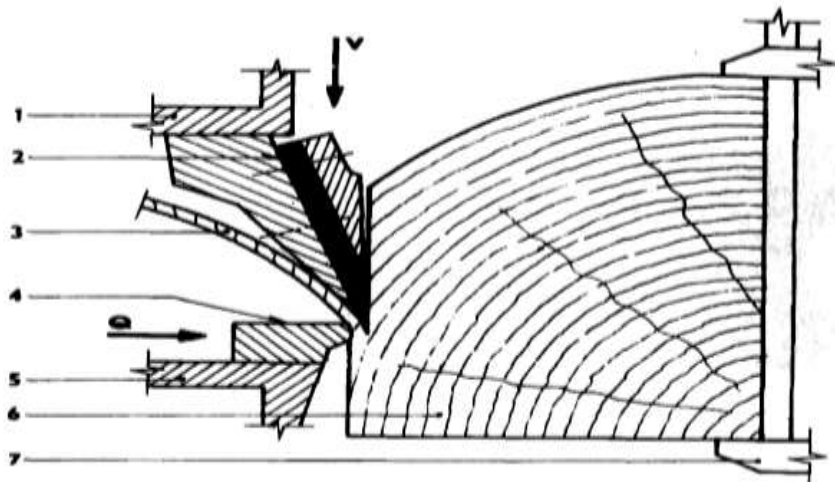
Схема отримання струганого шпону: 1 – ножовий пристрій; 2 – ніж; 3 – лист шпону; 4 – притискна лінійка; 5 – упор; 6 – заготовка; 7 – супорт з кріпленням
